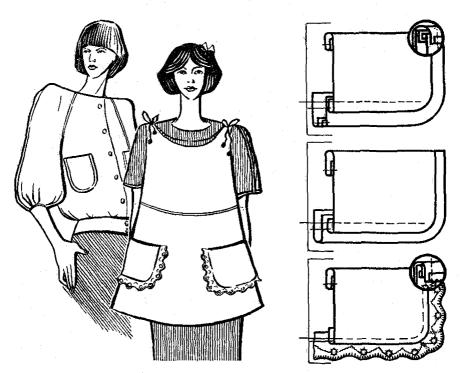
Накладной карман с бейкой, кантом, кружевом.
